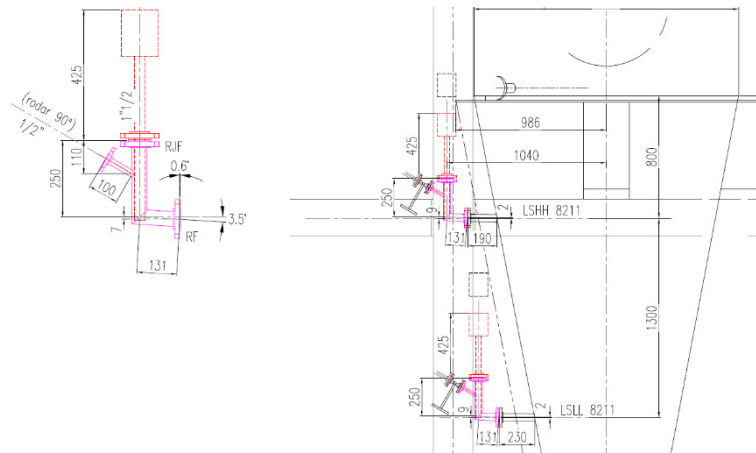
Desenho com acessório a construir e verificação de medidas após implantação
